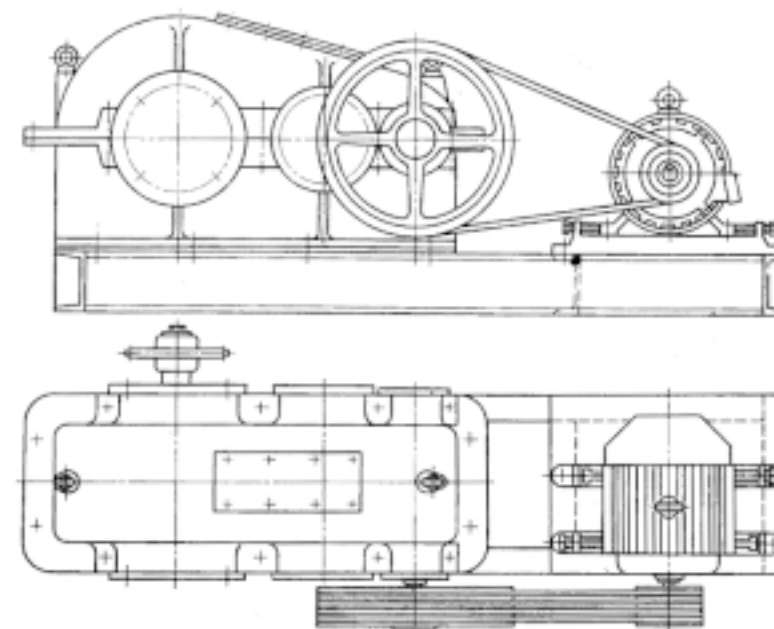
Общий вид привода с двухступенчатым цилиндрическим редуктором
